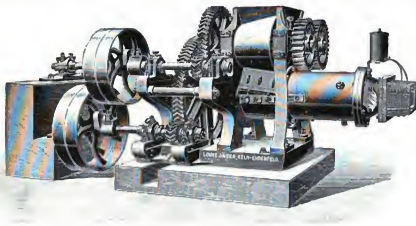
Ziegelmaschine von Louis Jäger, Cöln-Ehrenfeld.
